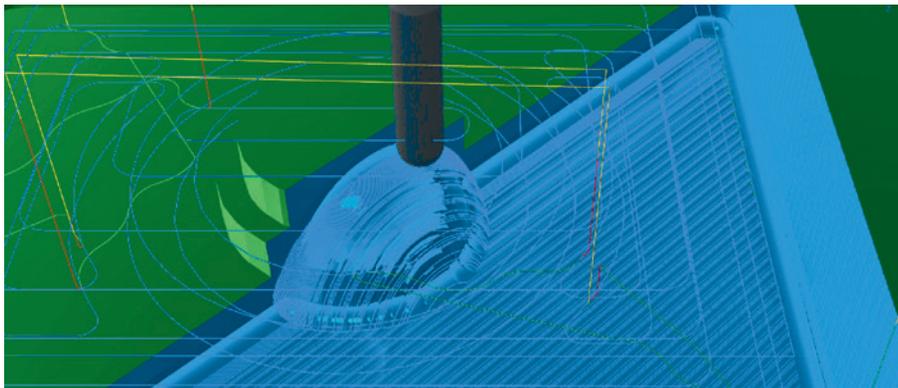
Erst mit 3D-Fräsen – und vielen eng gesetzten Fräsbahnen – lässt sich die Halbkugel sauber fräsen.
